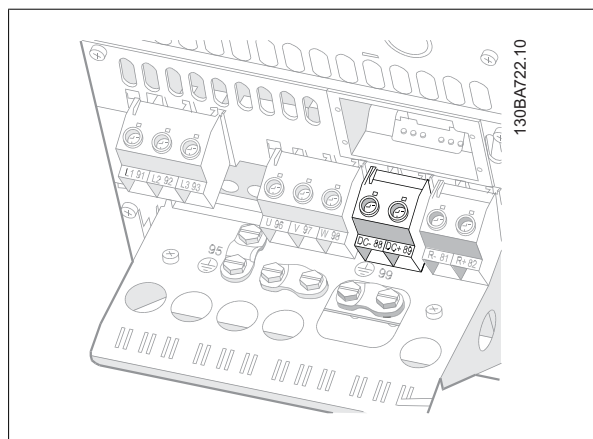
Conexões do barramento CC para o gabinete metálico B4.
